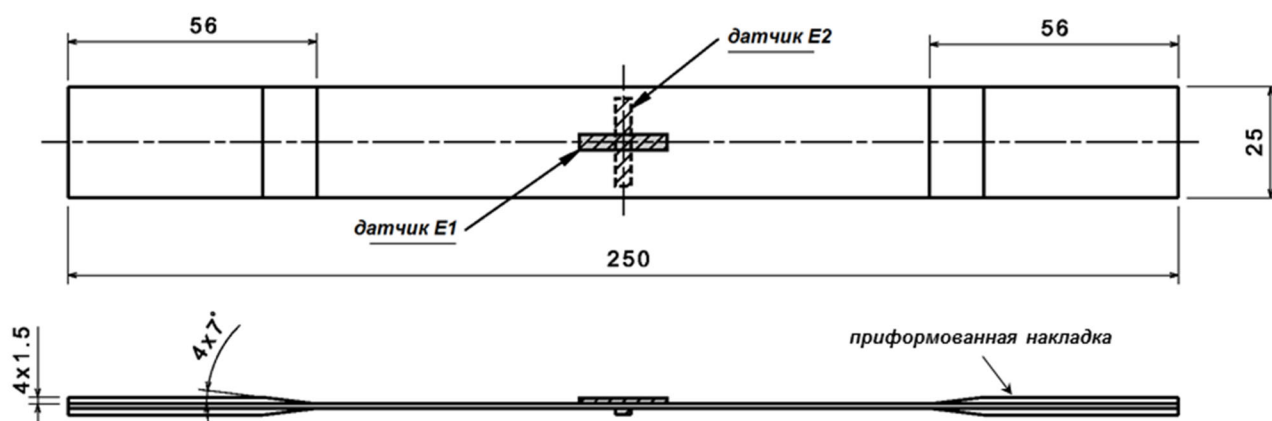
Эскиз образца для испытаний на усталость (размеры в мм)
